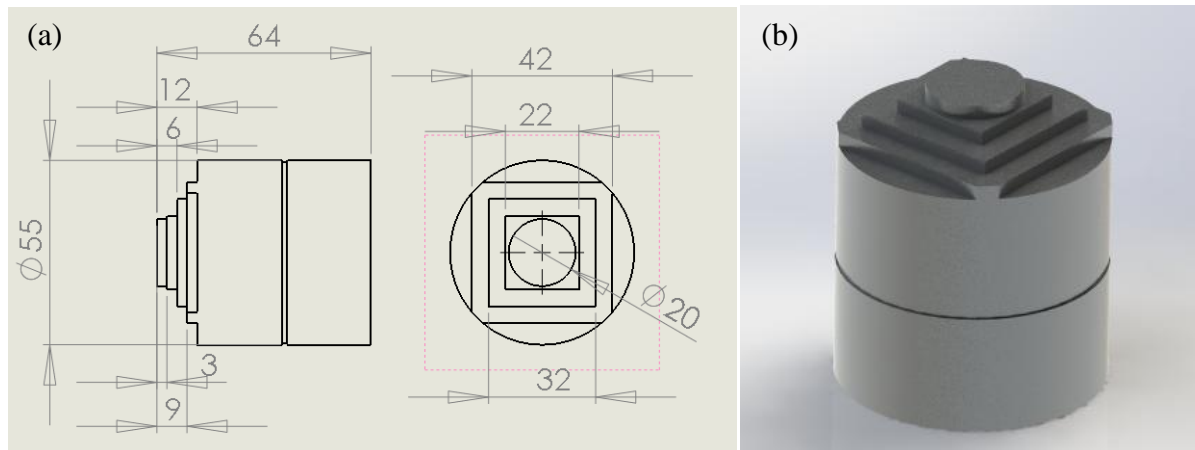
(a) Dimensões da Peça 1, (b) Representação 3D.
